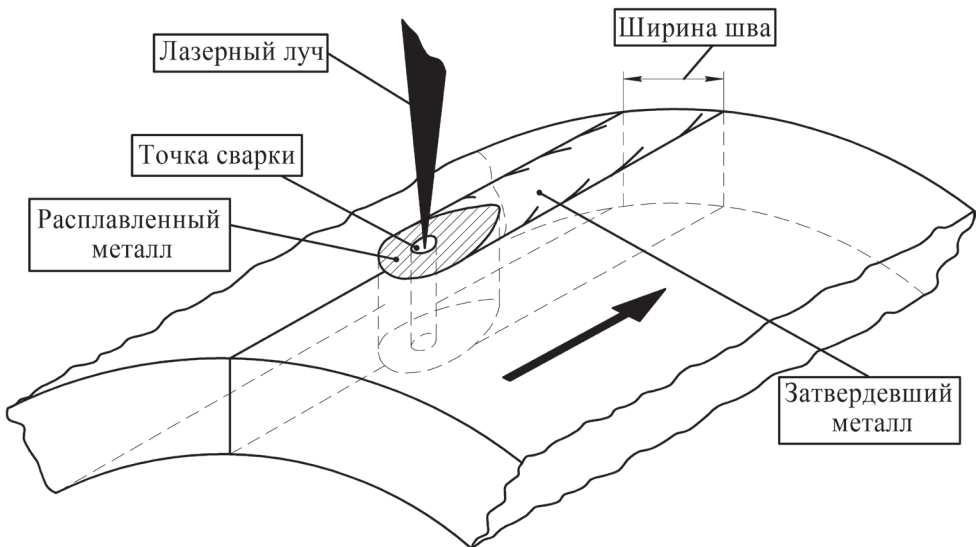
Зона сварного шва при лазерной сварке труб
